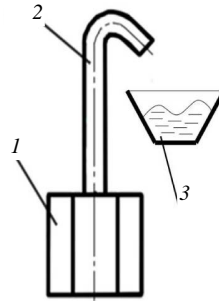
Контрольное приспособление: 1 – гайка; 2 – трубка высокого давления; 3 – емкость
